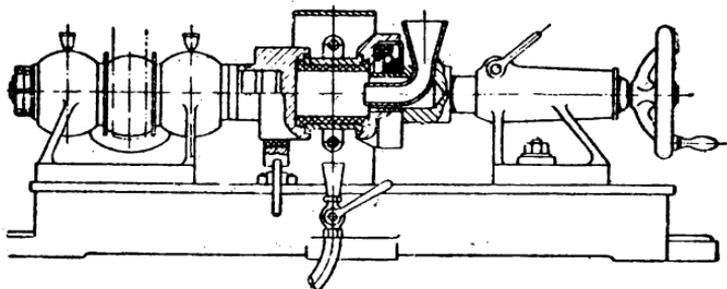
Установка для центробежной заливки вкладыша подшипника, собранная из деталей токарного станка.
